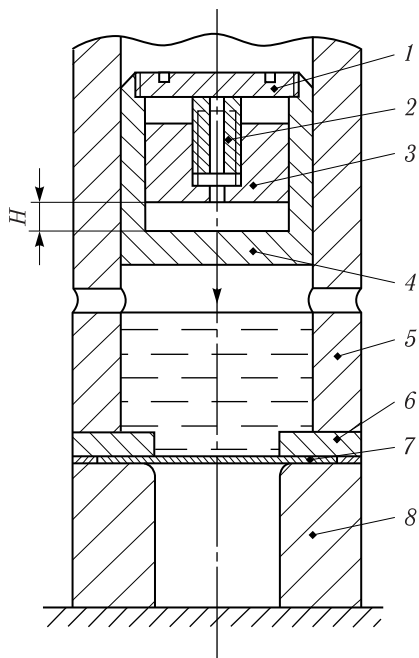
Схема устройства для осуществления процесса многоударной вытяжки: 1 — крышка бойка; 2 — регулировочный винт; 3 — вкладыш; 4 — корпус бойка; 5 — рабочая камера; 6 — гидродинамический прижим; 7 — заготовка; 8 — матрица
